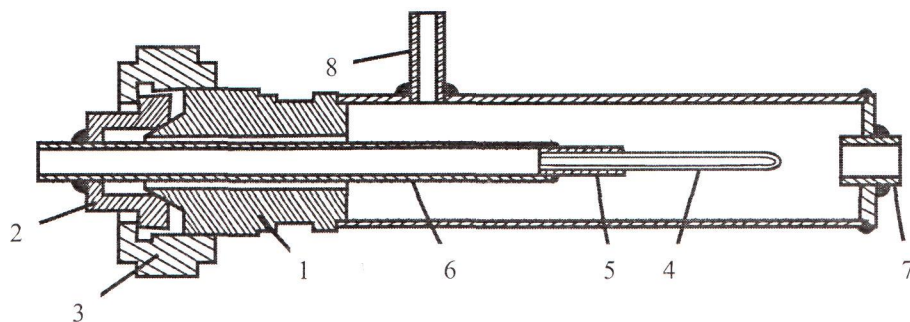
Сборочный чертеж диффузионного фильтра изотопов водорода: 1 – штуцер; 2 – ниппель; 3 – гайка; 4 – диффузионный элемент; 5 – коллектор; 6 – отвод чистого водорода; 7 – патрубок подачи водородсодержащей газовой смеси; 8 – патрубок отвода примесей
